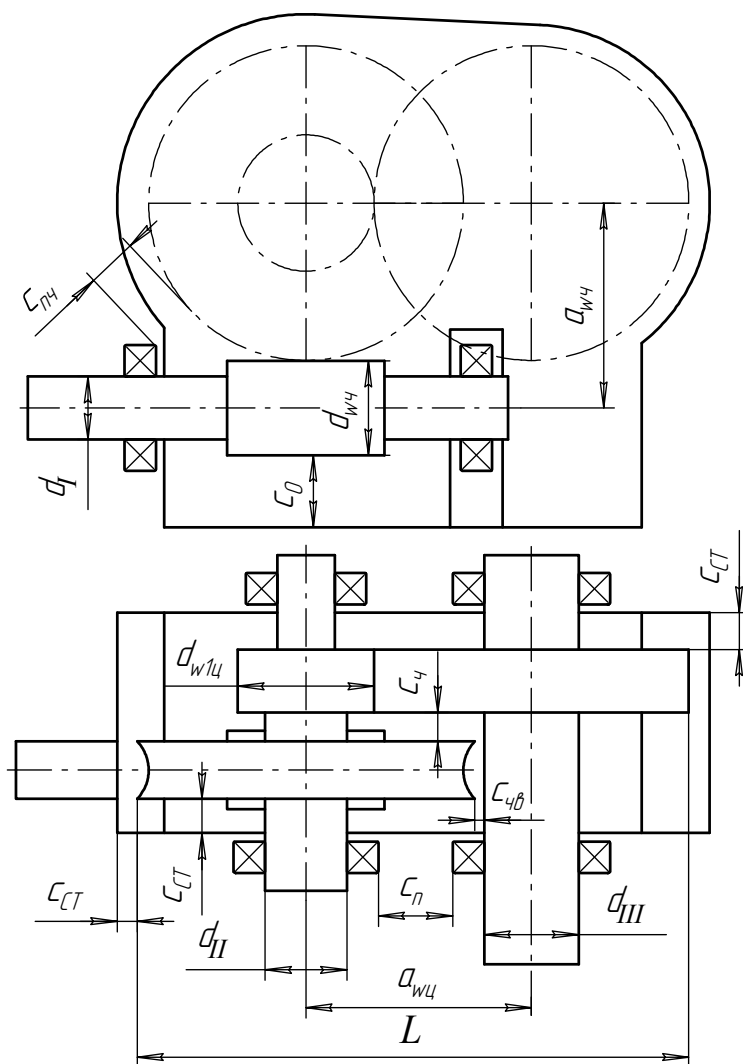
Расположение колёс и подшипников червячно-цилиндрического редуктора
